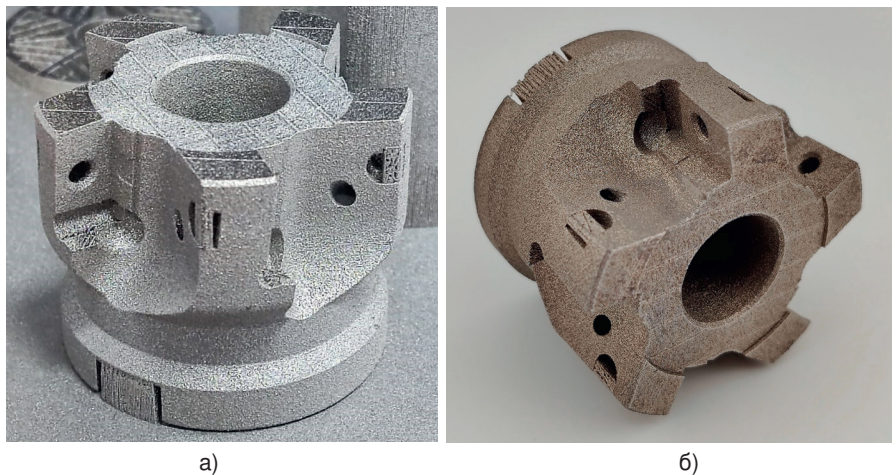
Внешний вид корпуса фрезы после аддитивного построения: а — на подложке as built; б — перед удалением поддержек
